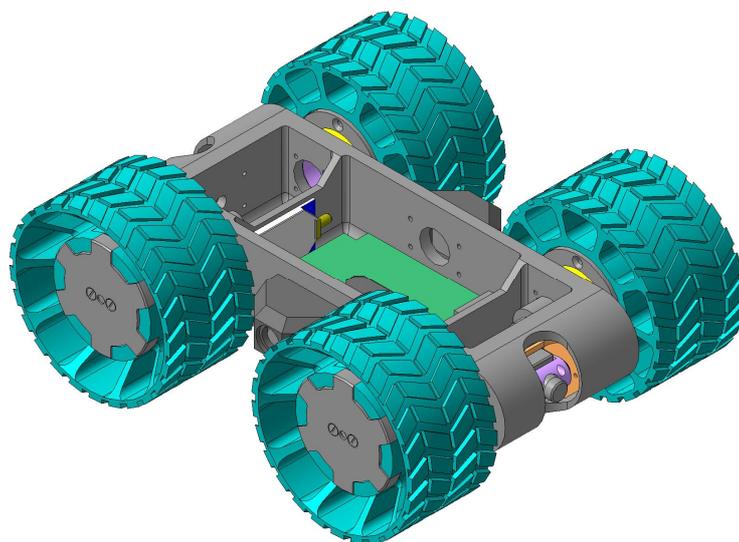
Конструкция корпуса и колес разрабатываемого робота. Крышка корпуса и АКБ не показаны
